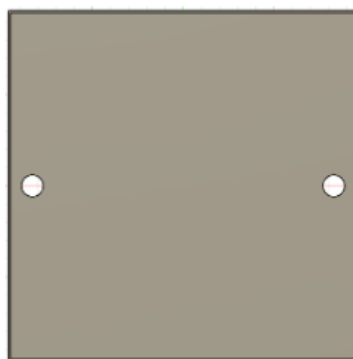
Especificações para a furação da placa ACM que será utilizada como parede, figura retirada do desenho técnico.
